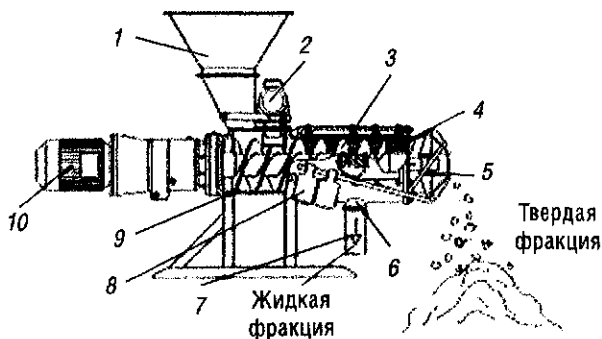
Схема прессошнекового сепаратора для навоза FAN PSS
